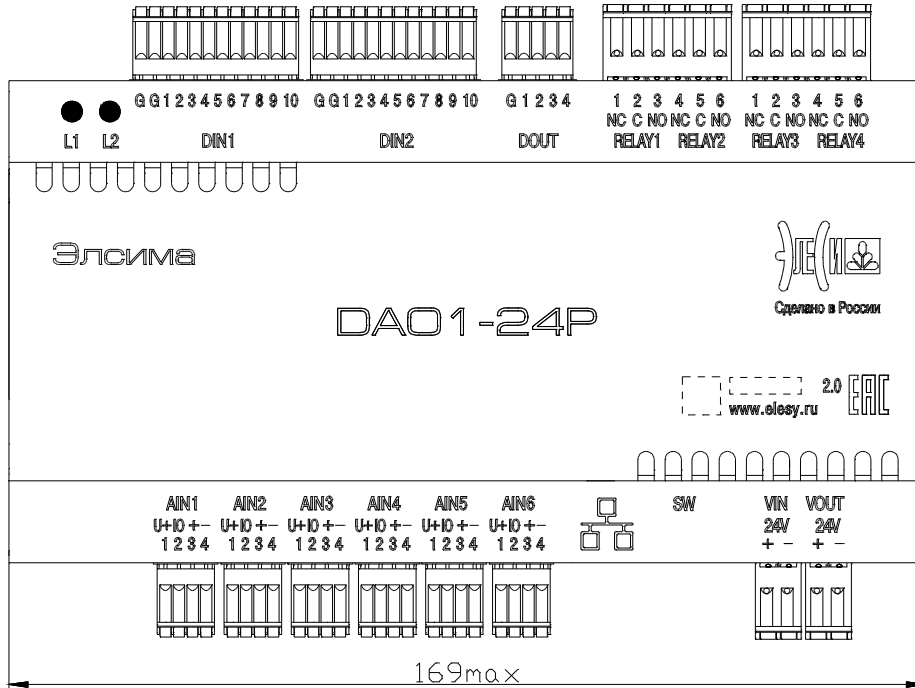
Модуль УВВ. Габаритный чертеж. Вид спереди
